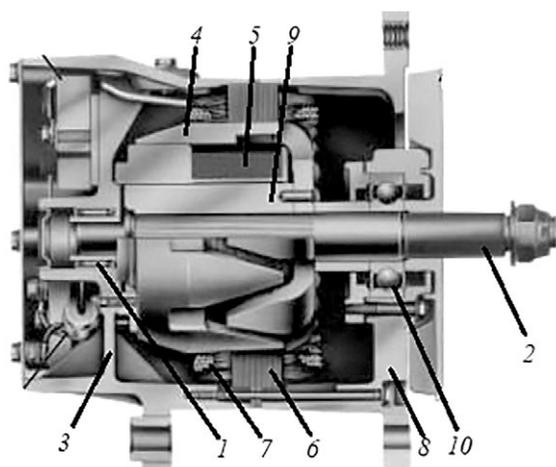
Разрез генератора Delco Remy серии 30-si тип 400: 1 — игольчатый подшипник; 2 — вал; 3 — задняя крышка; 4 — полюса; 5 — обмотка возбуждения; 6 — статор; 7 — обмотка статора; 8 — передняя крышка; 9 — магнитопроводящая втулка; 10 — передний подшипник.
